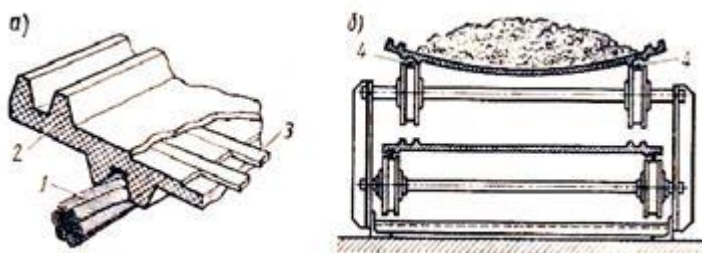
Стрічково-канатний конвеєр: а – стрічка; б – поперечний переріз конвеєра
